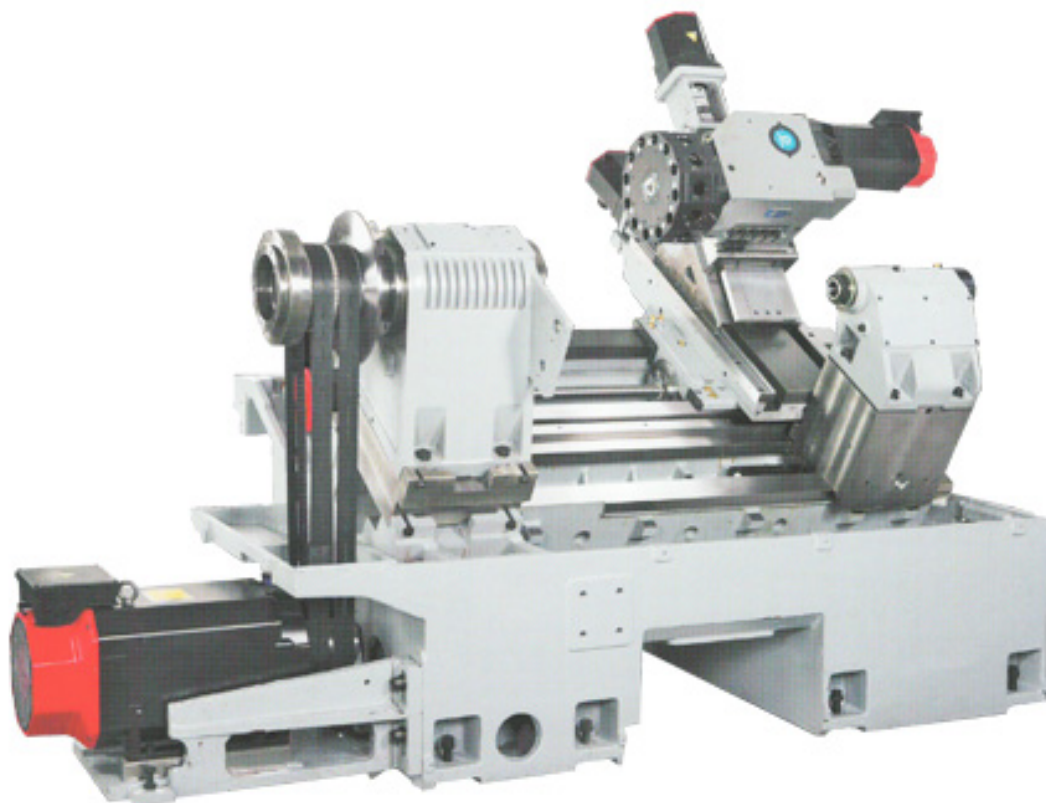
Горизонтальний токарний верстат UT-300SM
